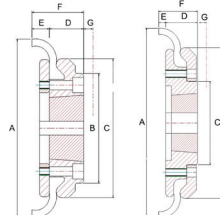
PLATEAUX D'ACCOUPEMENT PNEU INTÉRIEUR TYPE F
